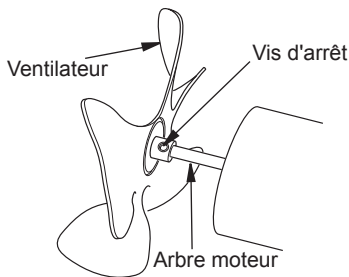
Emplacement du ventilateur, de l'arbre moteur et de la vis d'arrêt
